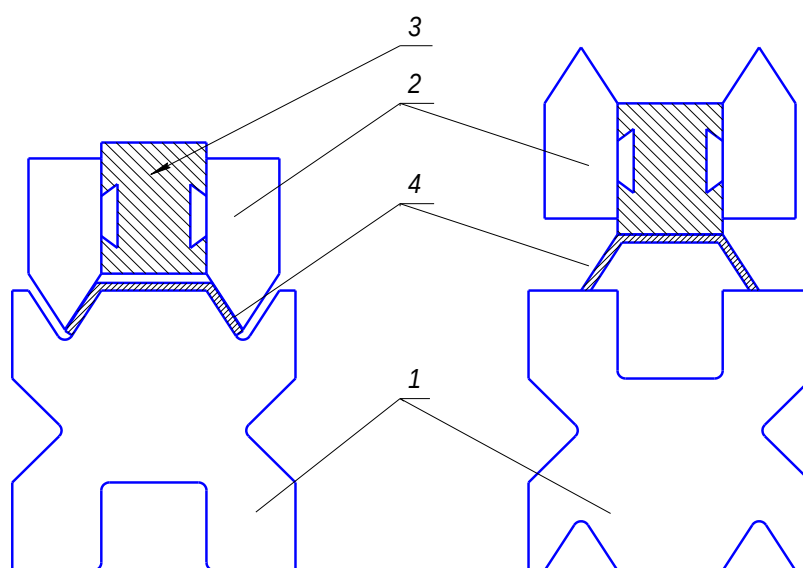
Універсальний комплект інструментів для згинання
